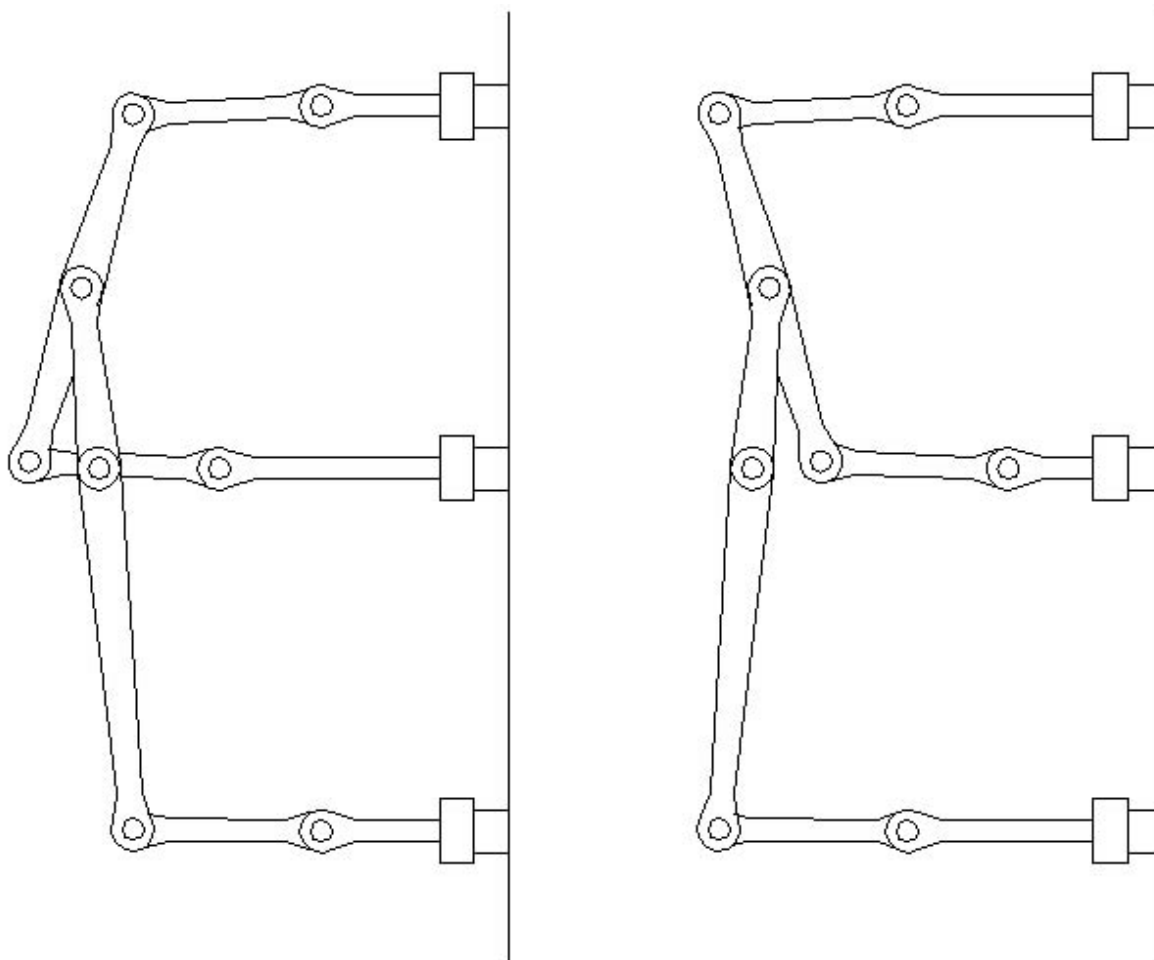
Distribución Gresley. Vista en planta de las palancas de comando
